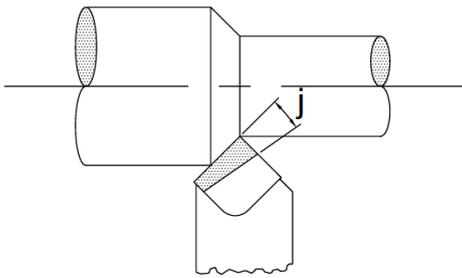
Отрицательный угол при вершине для черновой обработки
